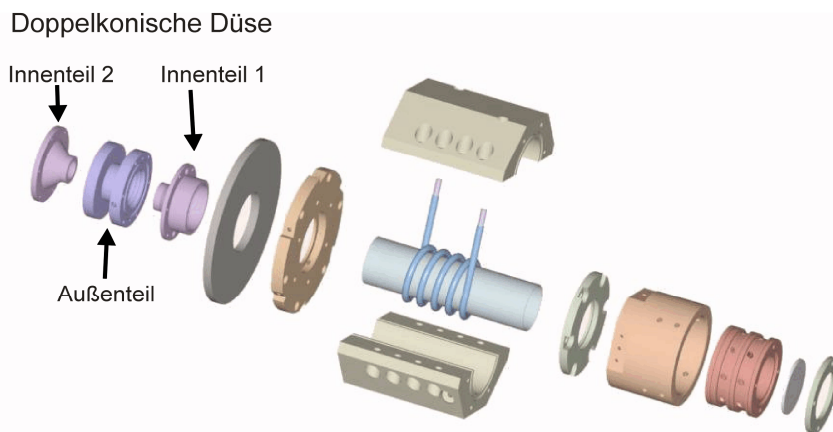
Explosionszeichnung des IPG4 (hier mit doppelkonischer Düse)
